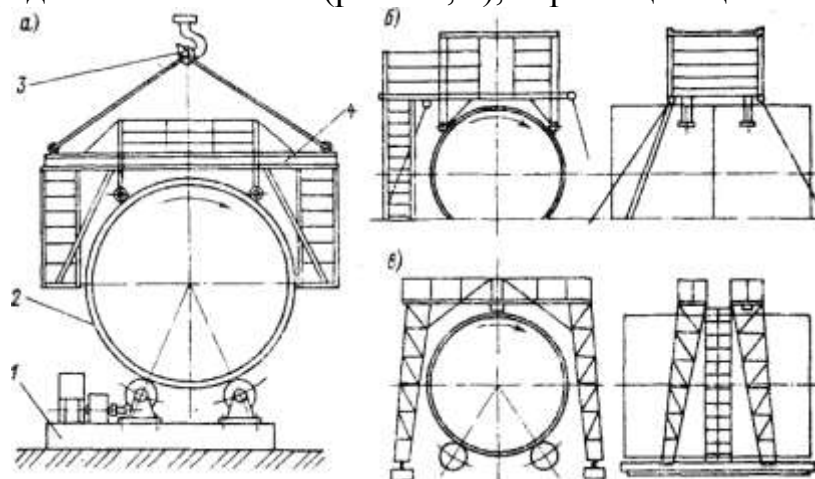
Установка для сварки кольцевых стыков блоков цементных печей
